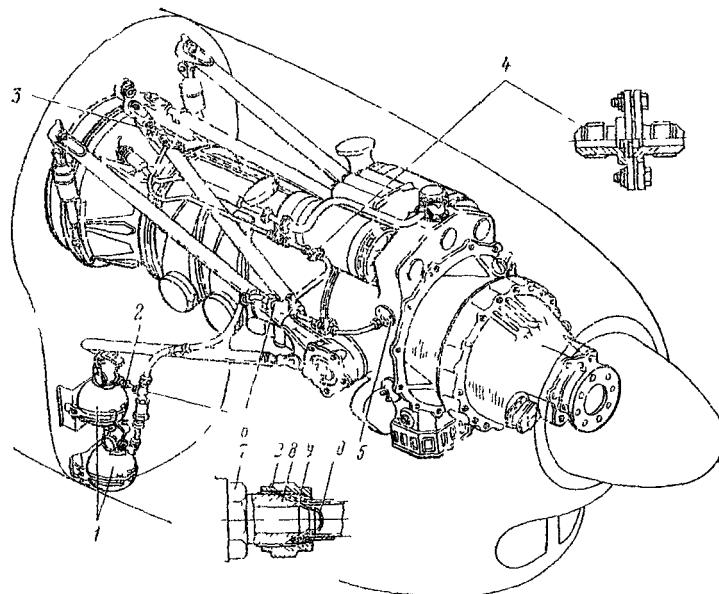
Полумонтажная схема противопожарной системы двигателей:
